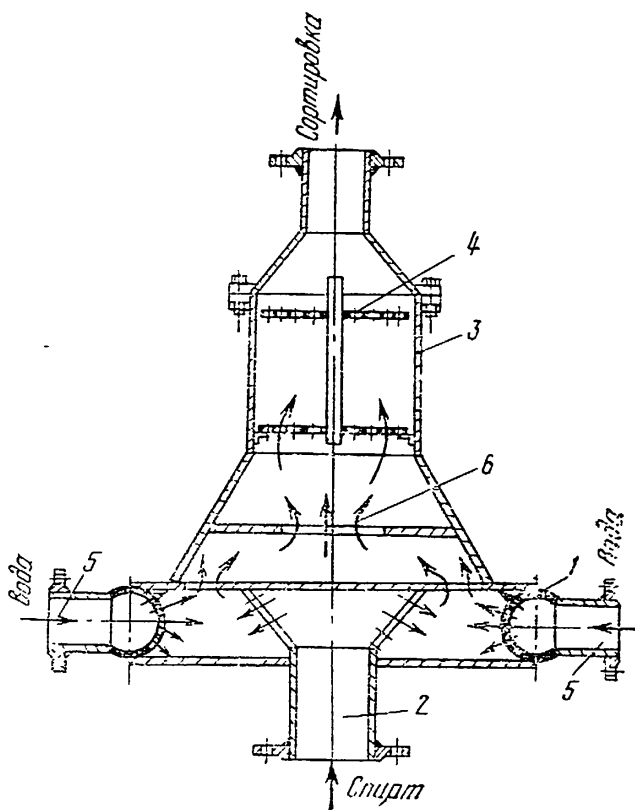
Смеситель непрерывного действия конструкции ВНИИПрБа.
